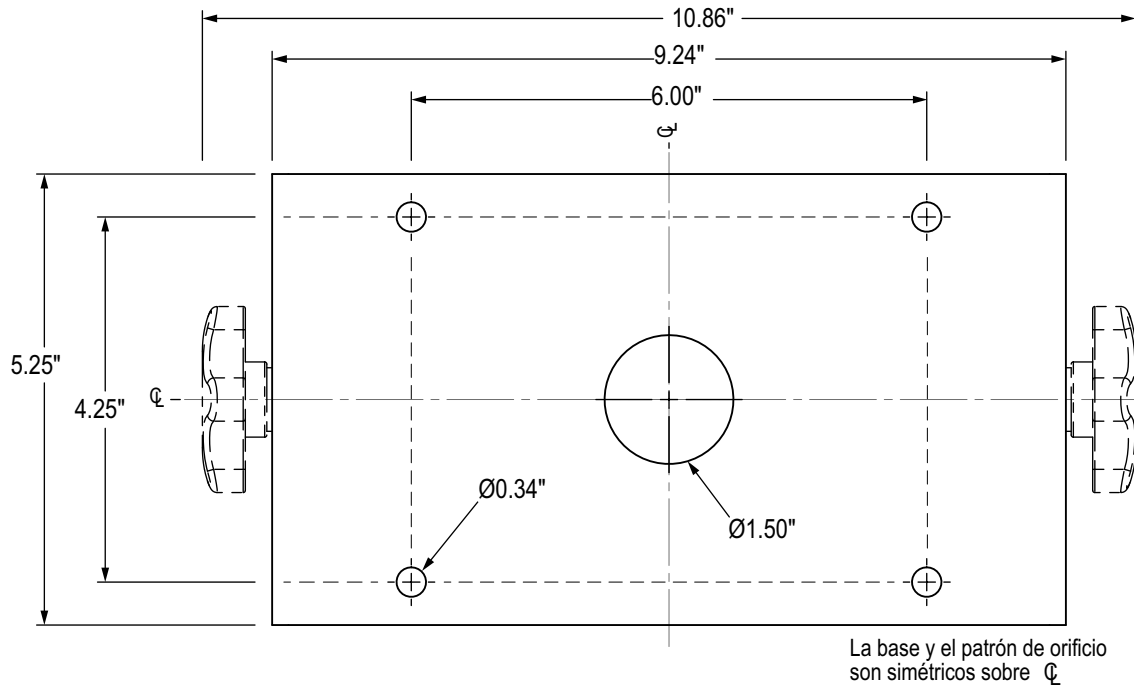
Dimensiones del patrón de orificios de la base inclinable universal
